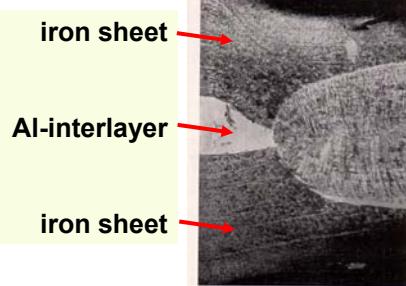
Eisenblech mit Aluminiumzwischenlage, Punktschweißung Vergr. = 35 (30)
